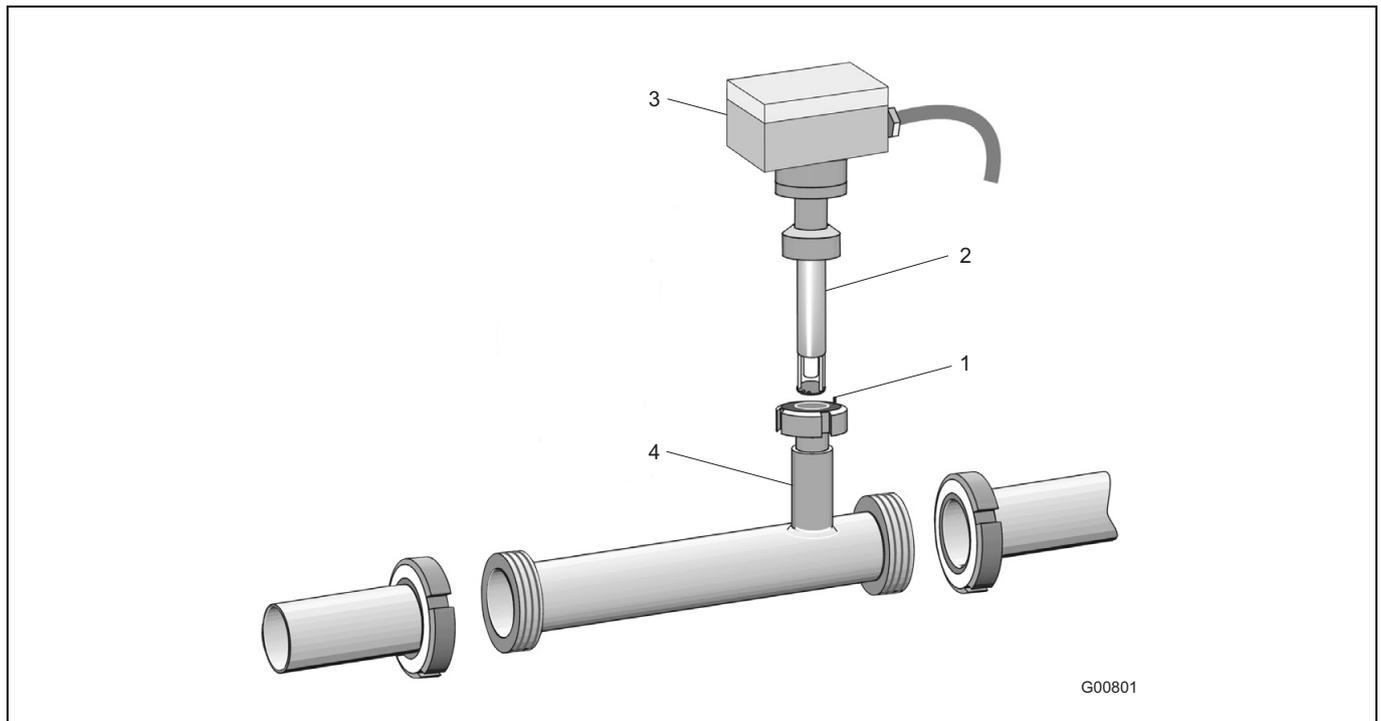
Prozessanschlüsse mit Rohrverschraubung S nach DIN11851. Messwertaufnehmer und Rohrbauteil auch mit FG-Flanschen möglich. FG-Flansche am Rohrbauteil sind immer beidseitig glatt (ohne Nut).
